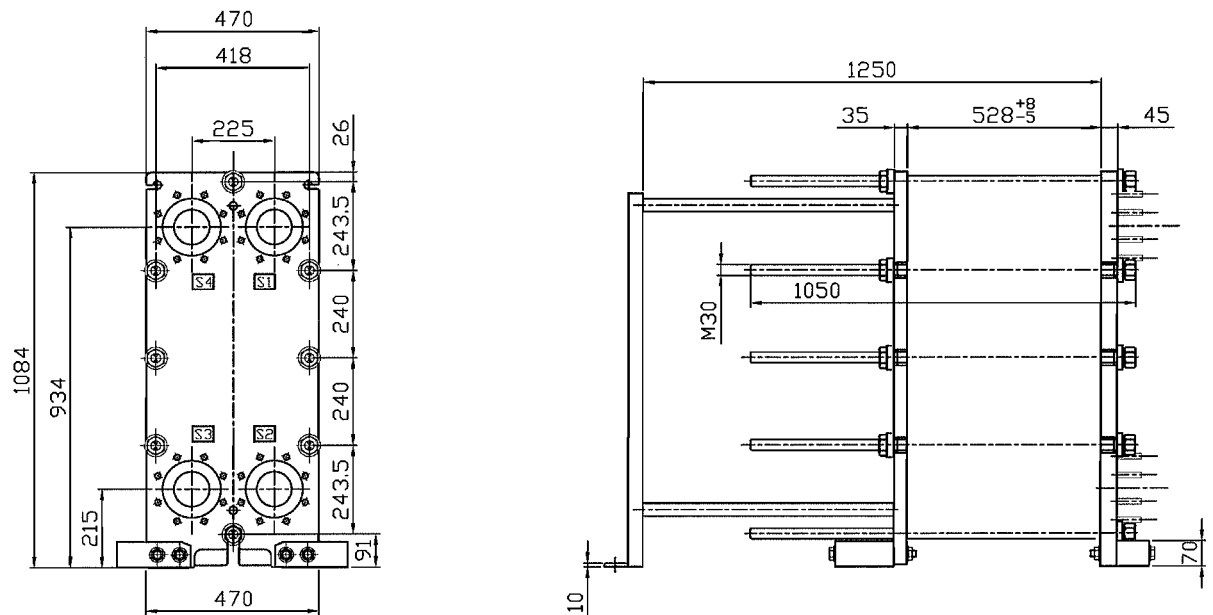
Габаритный чертеж подогревателя борсодержащих вод KBF10AC001
